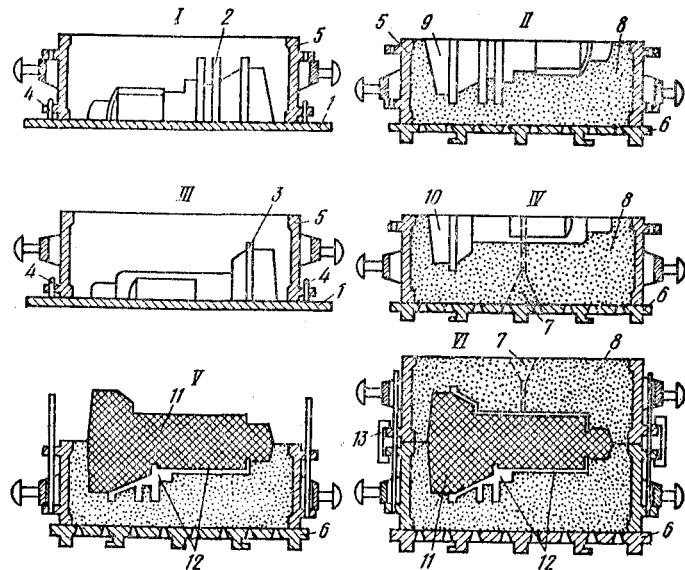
Схема последовательного изготовления песчано-глинистых форм на формовочных машинах:
